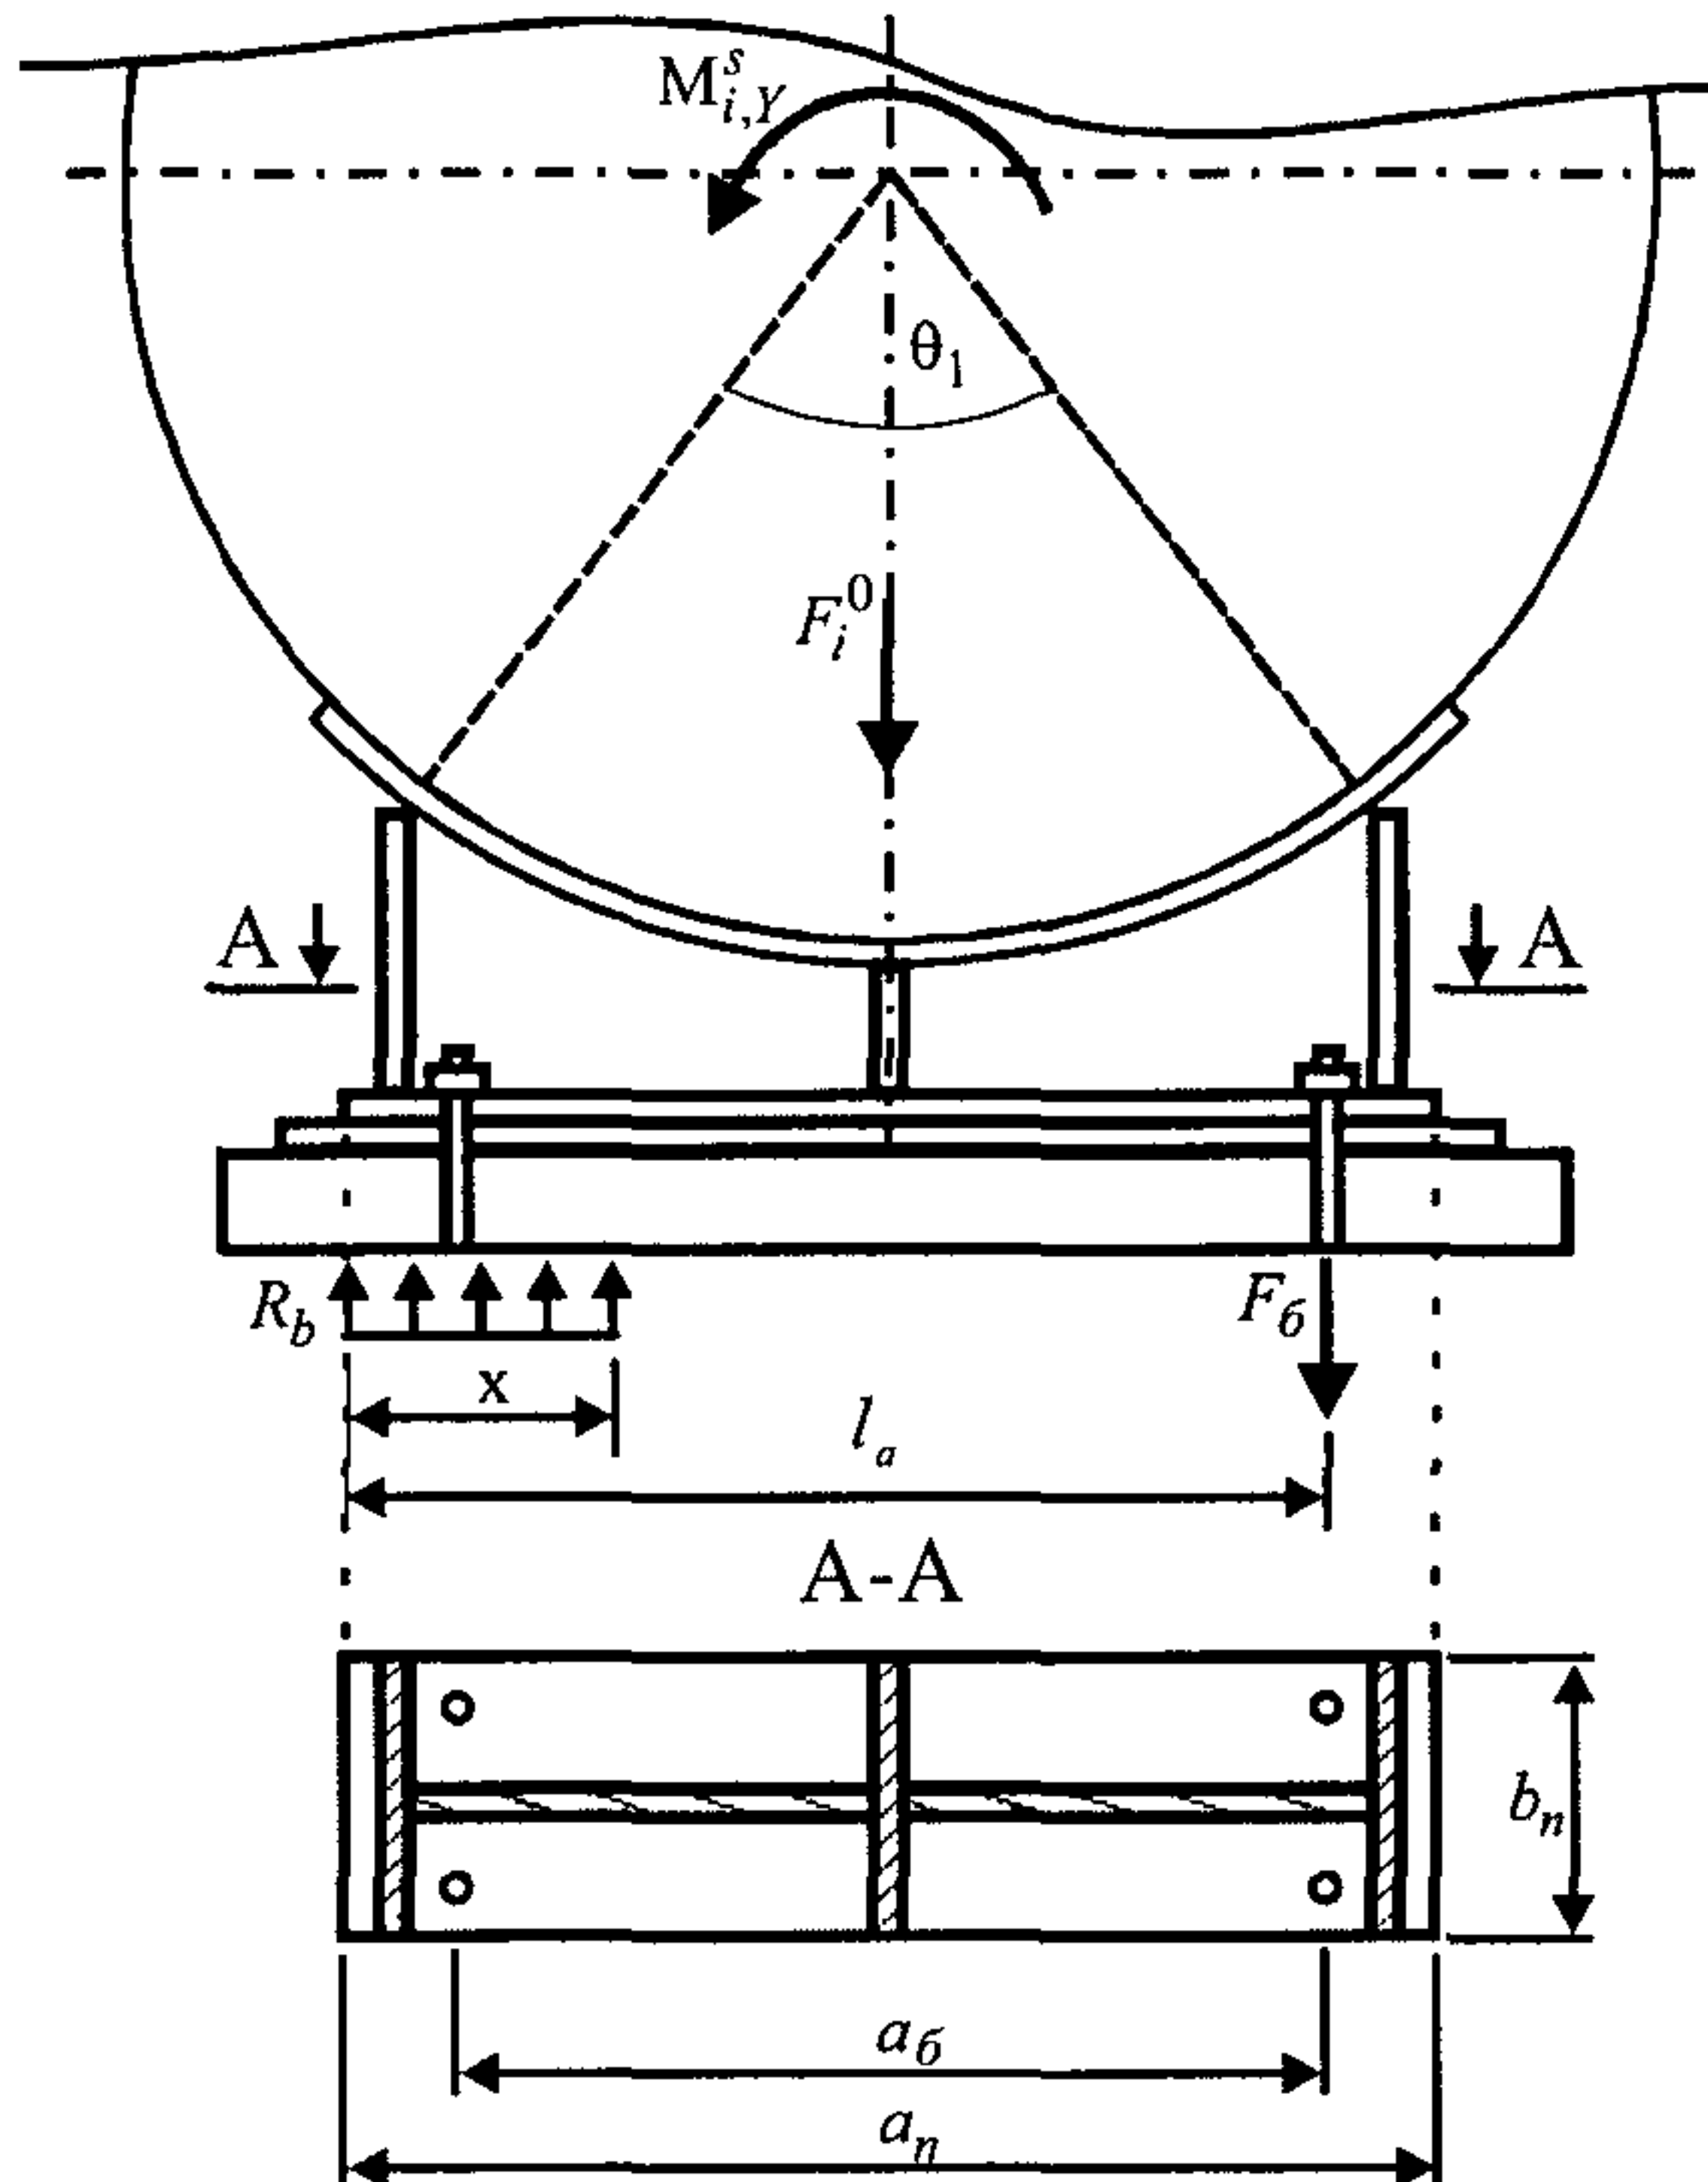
Расчетная схема для определения нагрузки на анкерные болты
